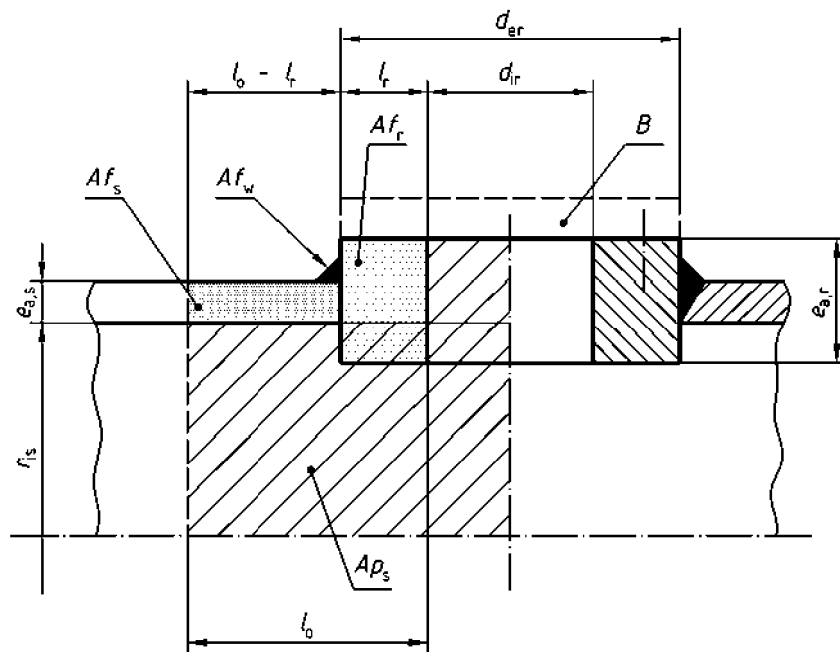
Envoltente cilíndrica con abertura aislada y anillo de refuerzo con brida externa ciega B
